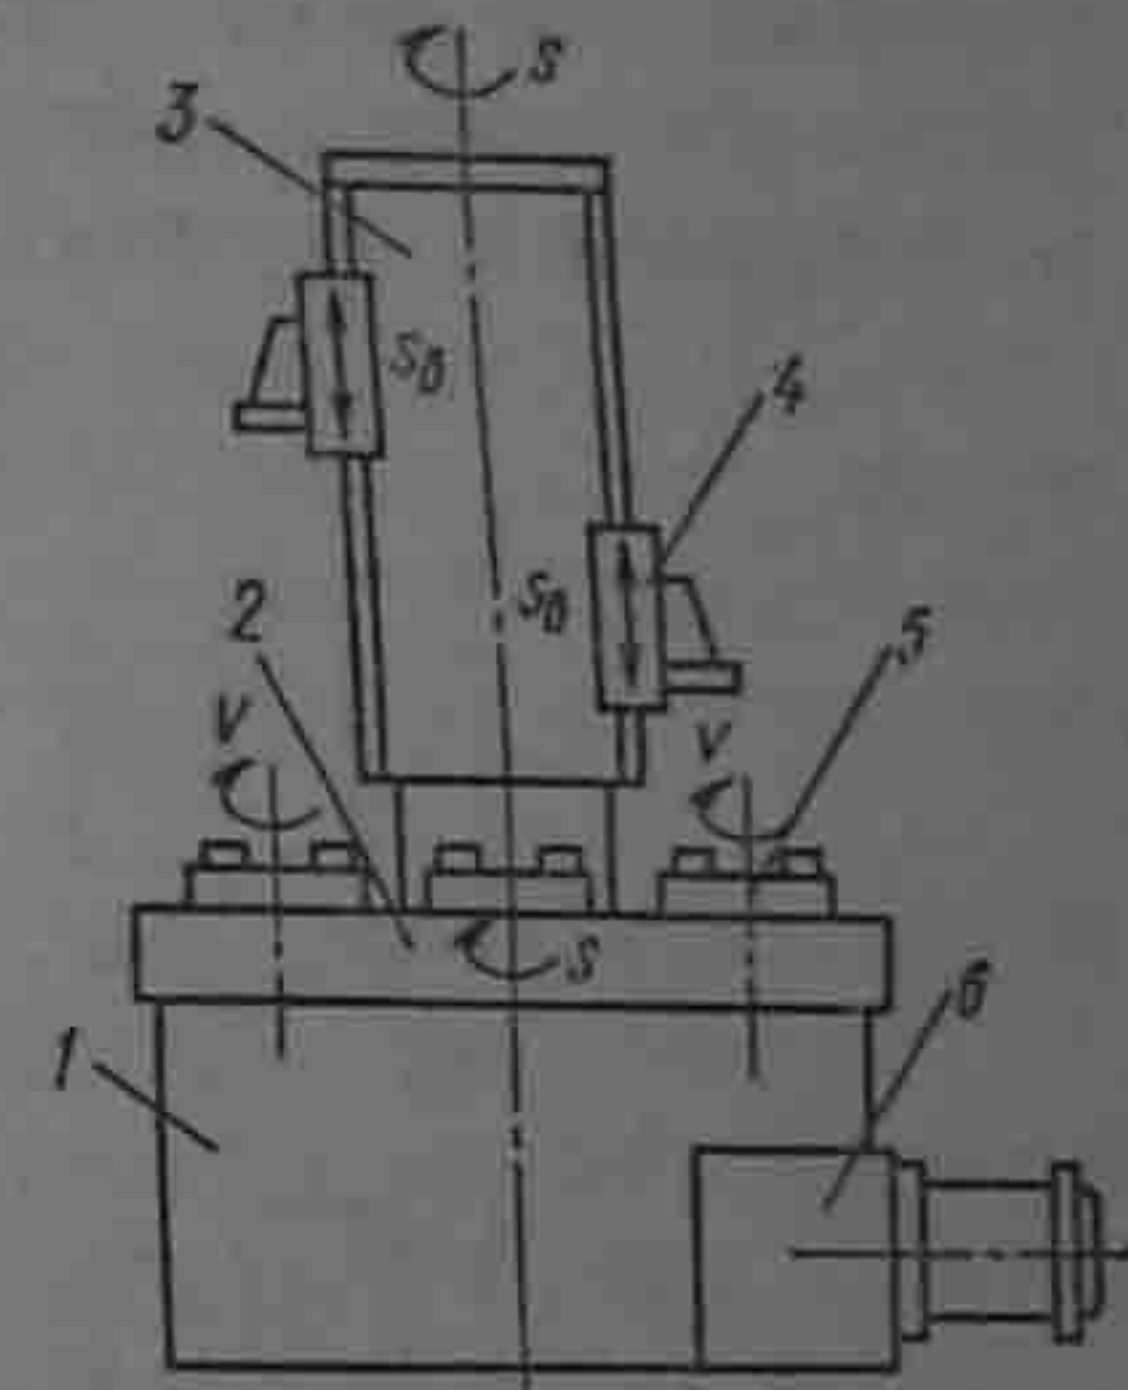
Общий вид многошпиндельного вертикального полуавтомата роторной обработки
